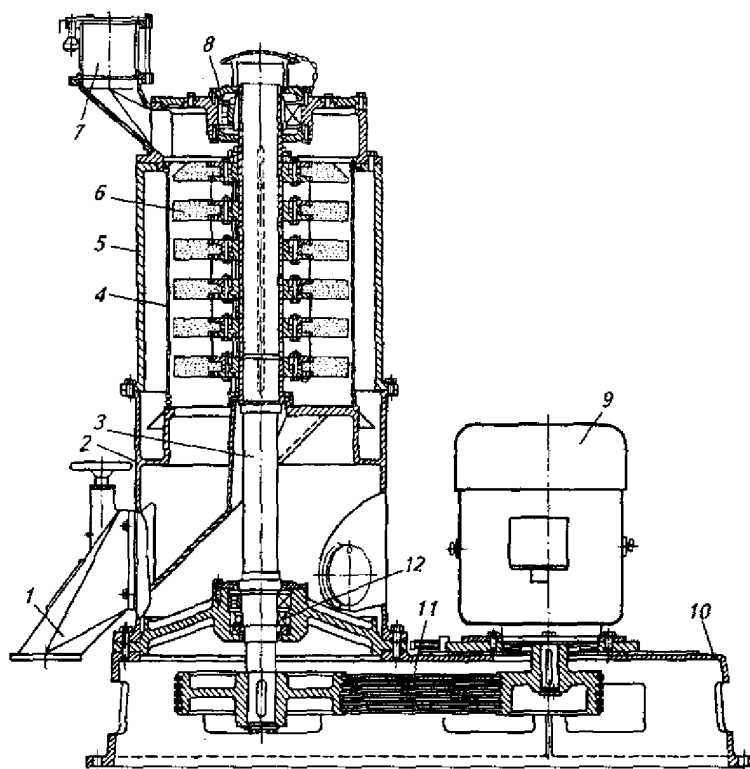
Шелушильно-шлифовальная машина А1-ЗШН-3: 1, 7- выпускной и приемный патрубки; 2 - корпус; 3 - вал; 4 - ситовый цилиндр; 5 - корпус рабочей камеры; 6 - абразивный круг; 8, 12 - подшипниковые опоры; 9 - электродвигатель; 10 - станина; 11 - клиноременная передача
